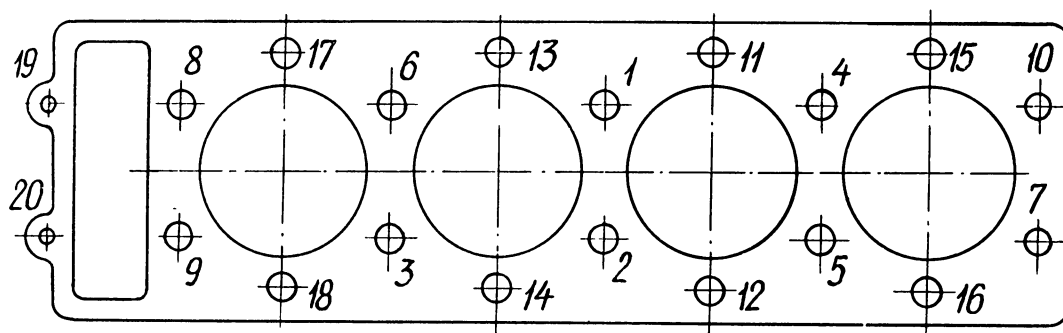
Порядок затягивания гаек крепления головки блока цилиндров
